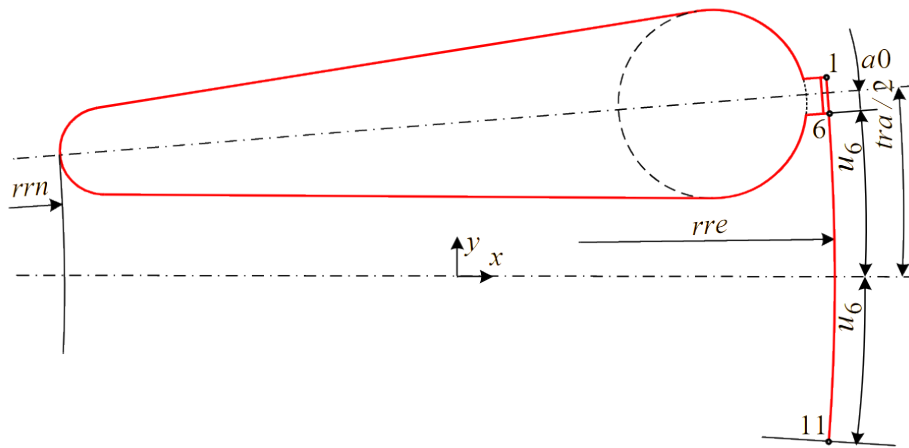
Повернутий зубцевий крок ротора для копіювання
